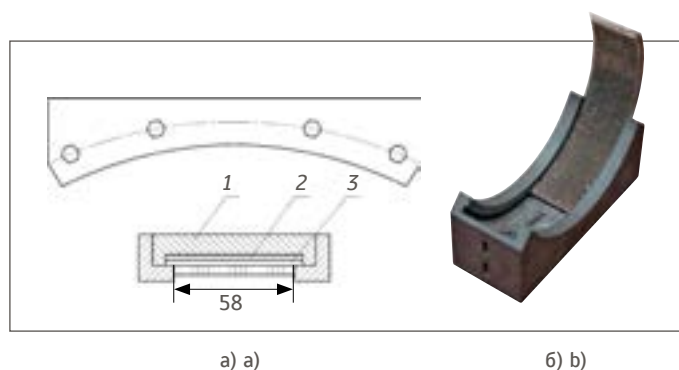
Приспособление для придания сотам вставкам изогнутой формы: а) схема, где 1 – корпус; 2 – прокладка; 3 – вставка; б) внешний вид
